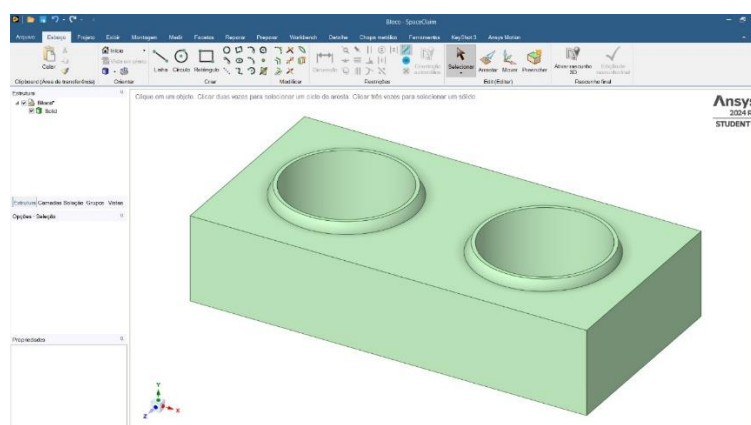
Bloco Estrutural (*SpaceClaim*).
